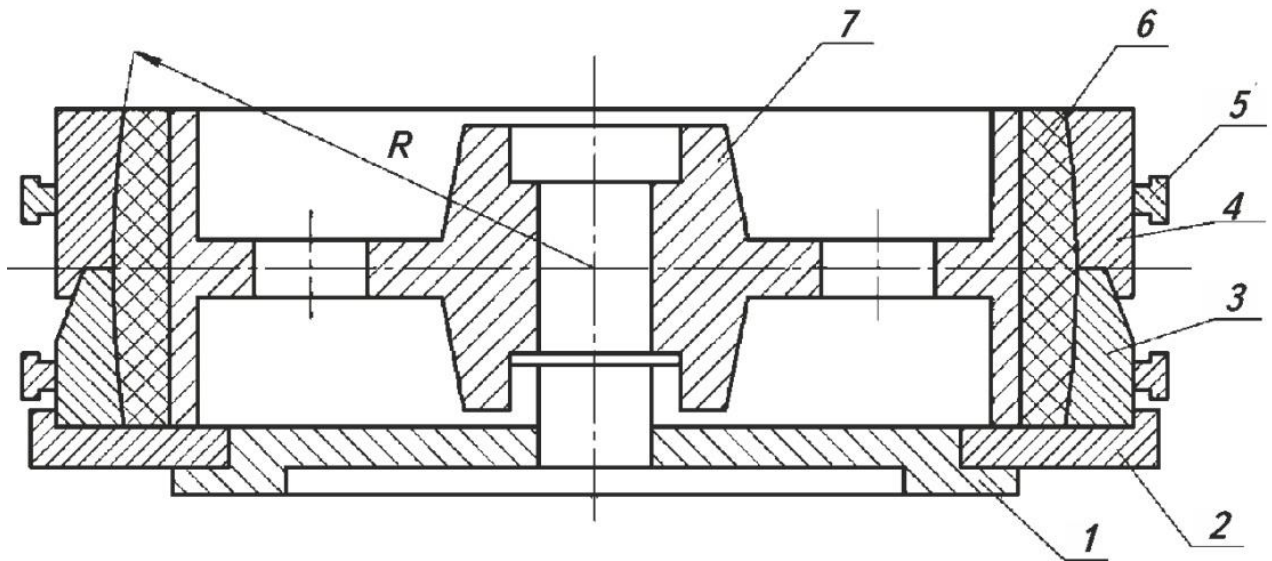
Форма для отливки сплошного упругого полиуретанового обода колеса погрузчика: 1 – центр; 2 – основание; 3 – нижняя полуформа; 4 – верхняя полуформа; 5 – захват; 6 – полиуретан; 7 – колесо
